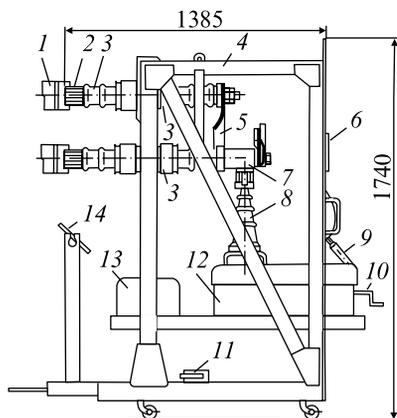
Выкатной переключатель станции стыкования ПСС-IV2: 1 — изолятор ячейки переключателя; 2 — ламели втычных контактов; 3 и 8 — неподвижный и подвижный изоляторы; 4 — каркас переключателя; 5 — гибкий шунт; 6 — смотровое окно; 7 — неподвижный контакт; 9 и 10 — рукоятки механизма доводки ручного привода (курбель); 11 — контакты заземляющего устройства; 12 — электропривод; 13 — блок управления; 14 — зеркало
